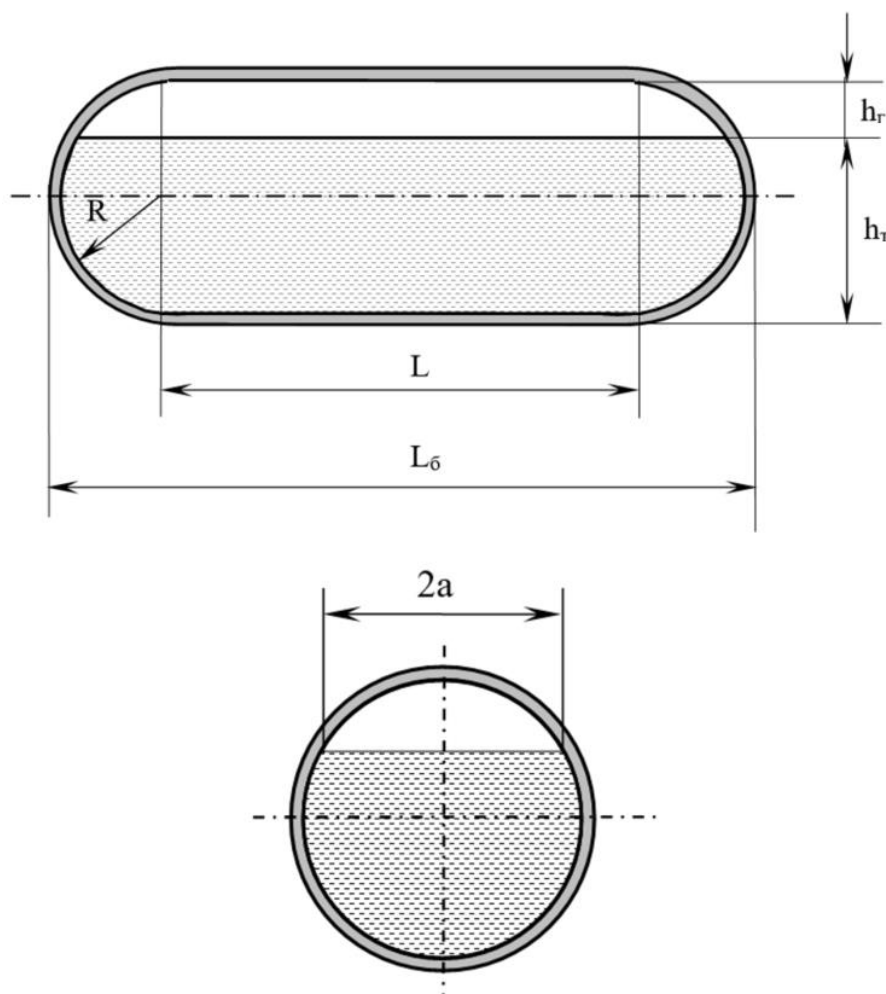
Схема цилиндрического топливного бака с торцевыми поверхностями в виде полусфер: $L_б$ -длина бака; h_r -высота газовой области в надтопливном пространстве бака; R -радиус полусферы ; $2a$ -хорда «зеркала» топлива.
